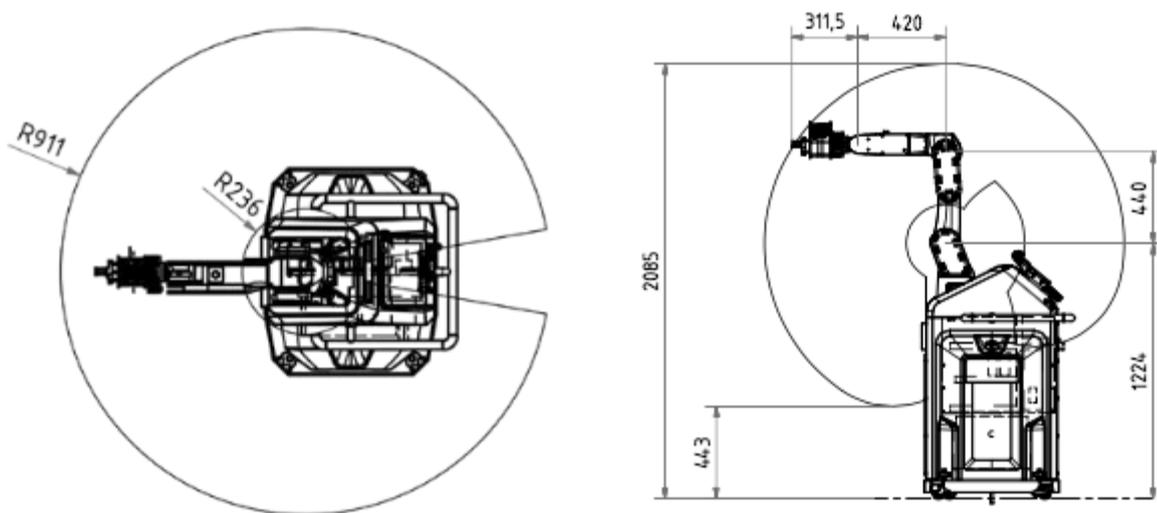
Spazio di lavoro (dimensioni in mm)
